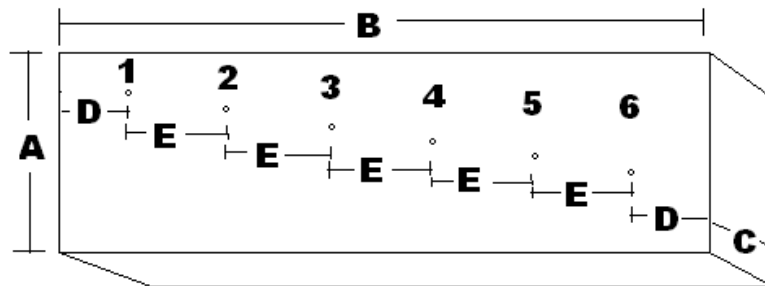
Esquema de las Fallas en la Placa de Acero [Autores]
